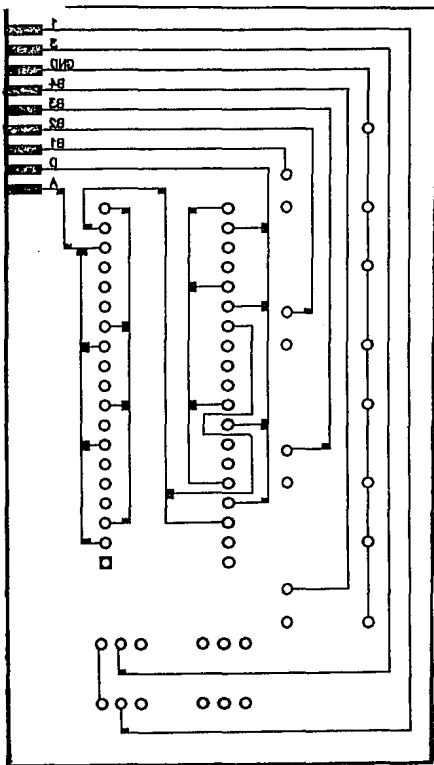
Displays del sistema, mascarilla de circuito impreso, lado de soldadura.
